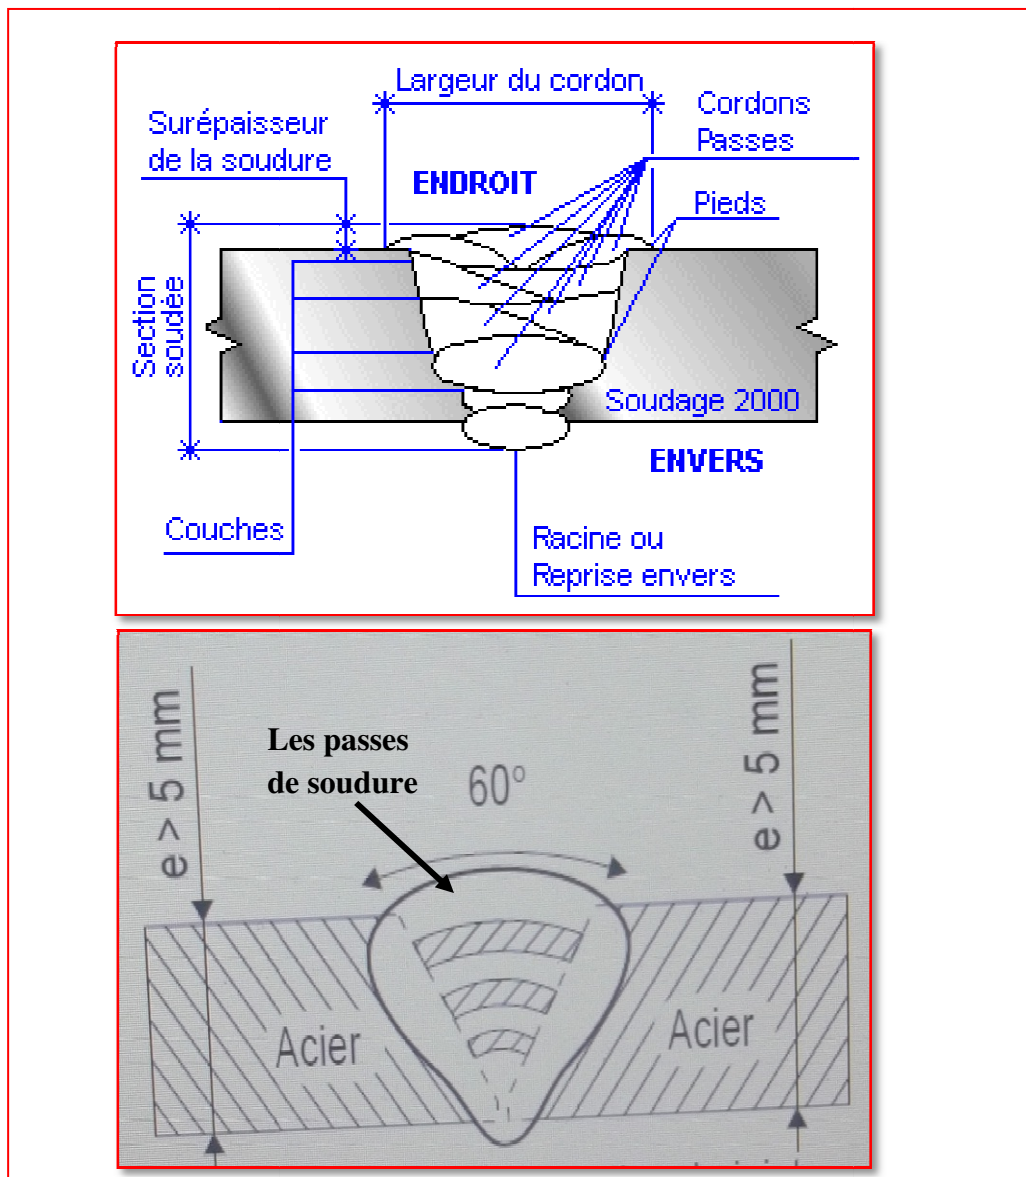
Enchaînement des passes de soudure [52,53].
